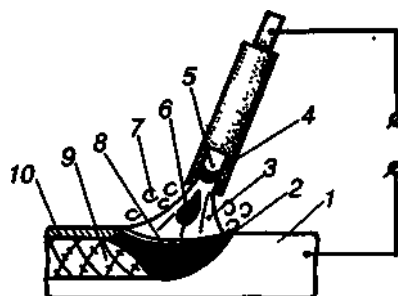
Схема процесса ручной дуговой сварки покрытыми электродами
